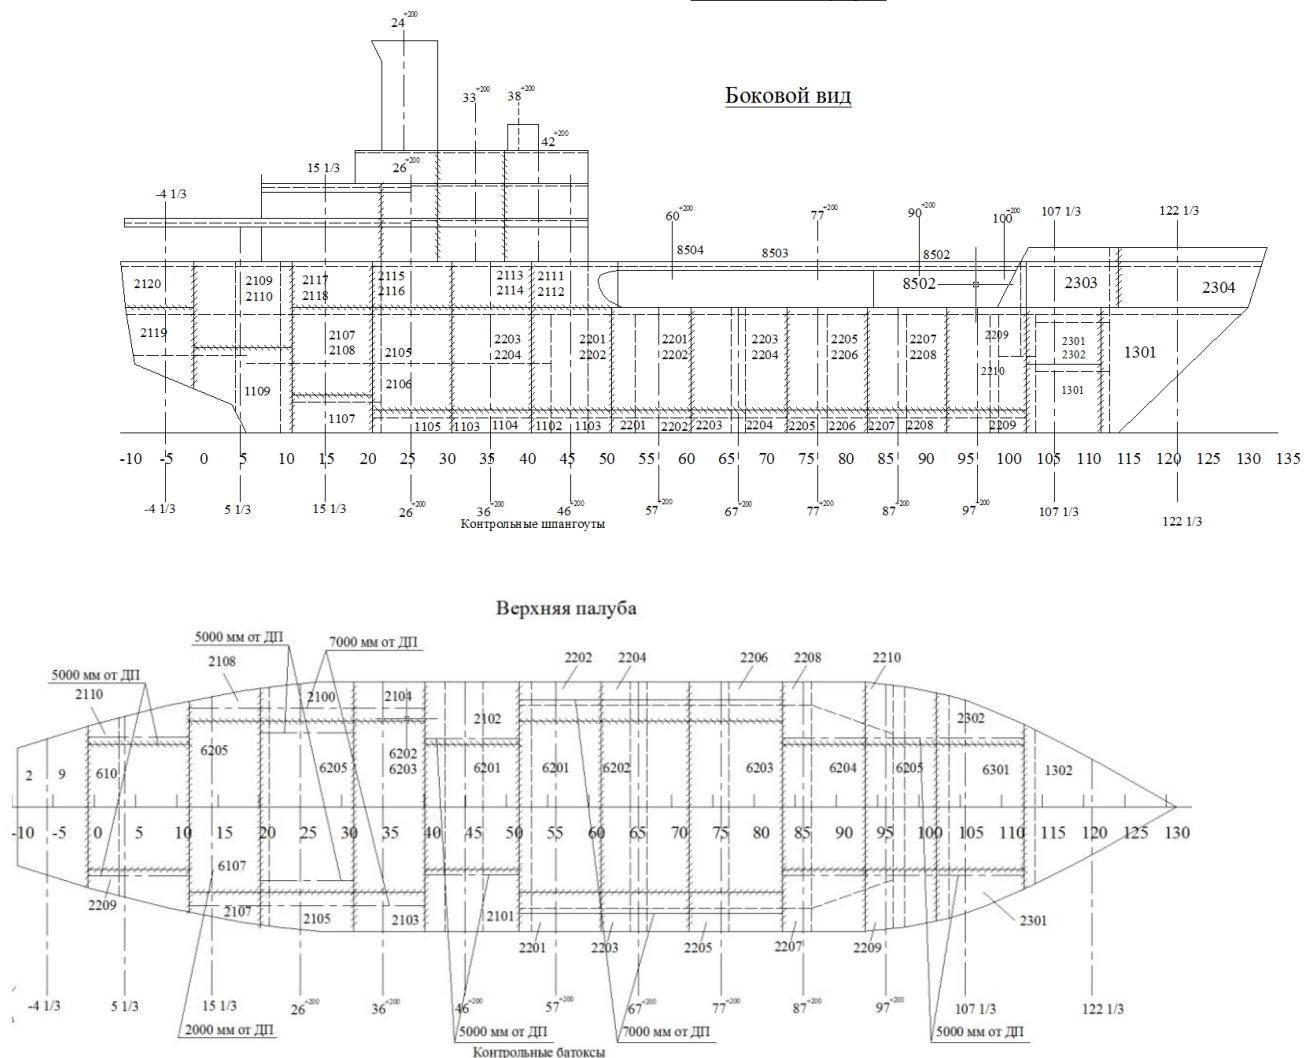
Пример выполнения чертежа разбивки корпуса на сборочные единицы
